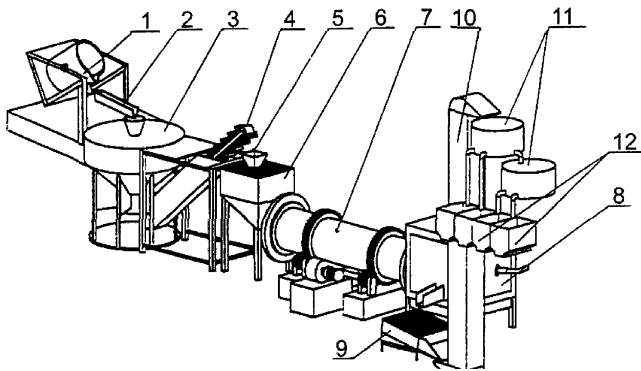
Схема комплекса оборудования для литья дробы мод. 46145: 1 – ковш; 2 – желоб металлоприемника; 3 – дробелитейная машина; 4 – наклонный элеватор; 5 – приемная воронка; 6 – бункер печи; 7 – барабанная печь; 8 – блок горелочной печи; 9 – агрегат рассева дробы; 10 – элеватор; 11 – вибросита; 12 – тара для сбора дробы по фракциям
